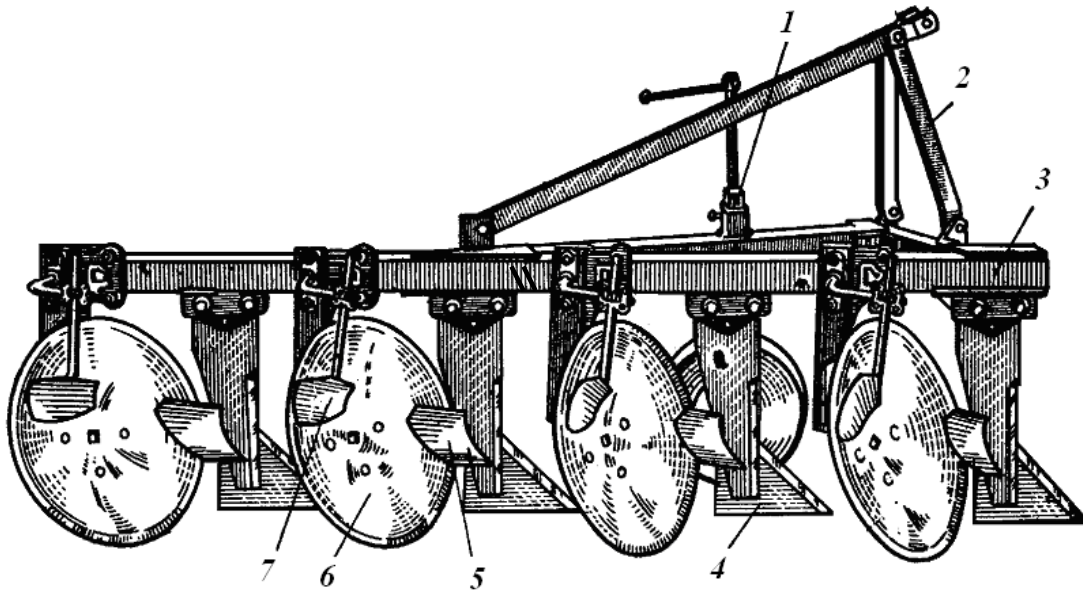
Плуг дисковий чотирьохкорпусний начіпний ПД-4-30: 1 - регулювальний механізм опорного колеса; 2 - начіпний пристрій; 3 - рама; 4 - розпушувач; 5 - передплужник; 6 - дисковий робочий орган; 7 - чистик
